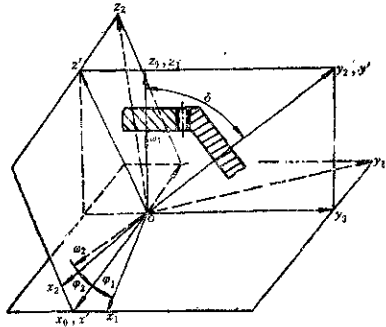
插齿刀加工非渐开线圆锥齿轮
